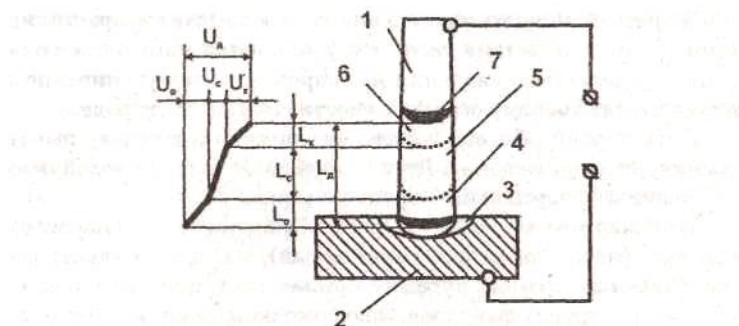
Схема сварочной дуги и падения напряжений в ней:
